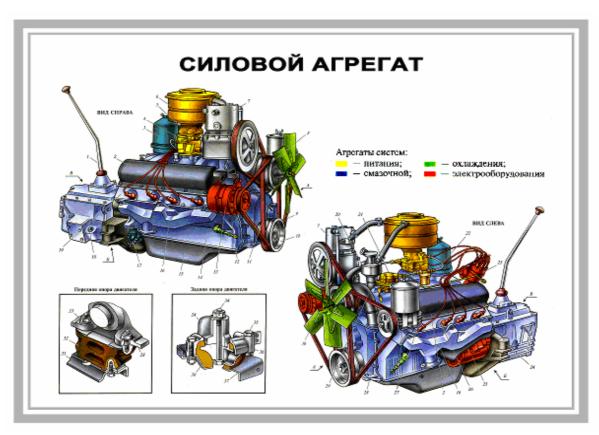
Силовой агрегат ЗИЛ-4333 А-двигатель; Б- сцепление; В-коробка передач
